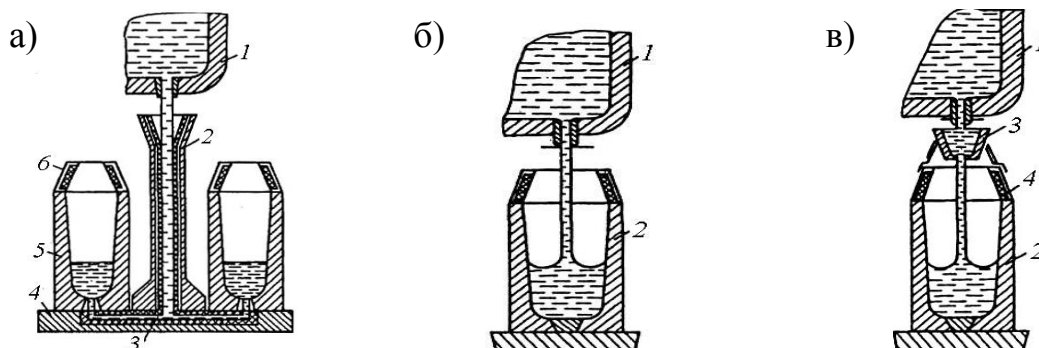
Схемы способов разливки стали: а – разливка стали сифоном:
